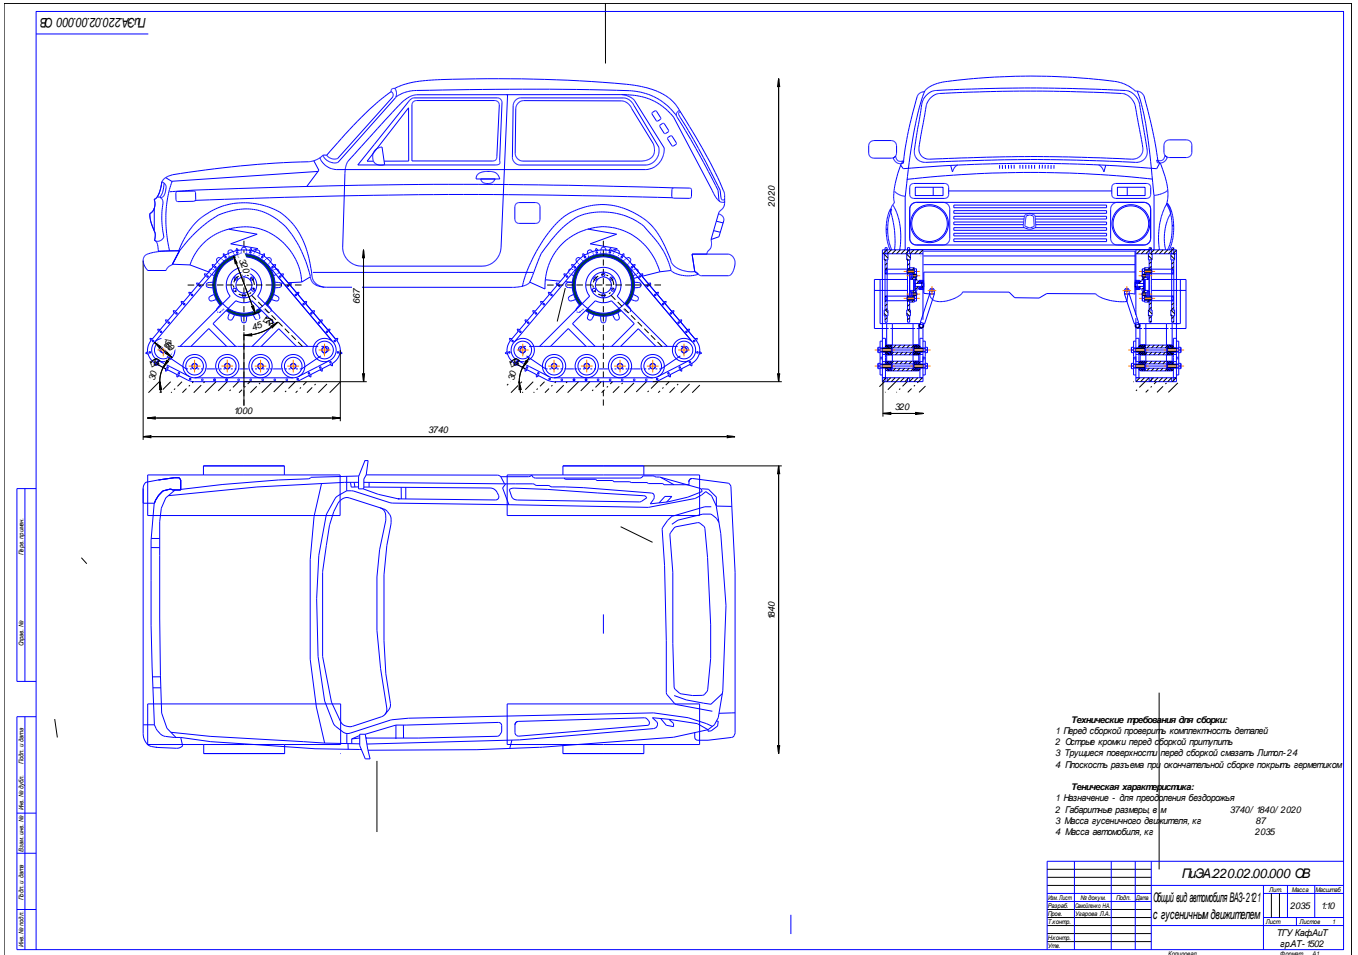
Гусеничный вездеход на базе автомобиля ВАЗ-2121
